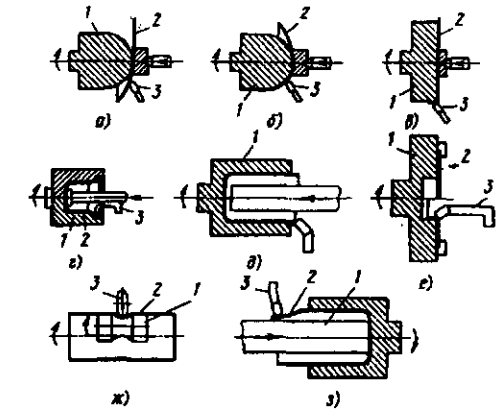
Основные виды ротационной вытяжки: а – в – обкатка; г, д – раздача; е – отбортовка; ж, з – обжим; 1 – оправка; 2 – заготовка; 3 – инструмент
